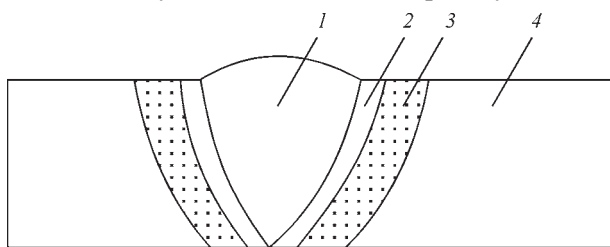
Схема будови структури металу зварних швів: 1 – зварний шов; 2 – зона сплавлення; 3 – зона термічного впливу (ЗТВ) зварювання; 4 – основний метал
